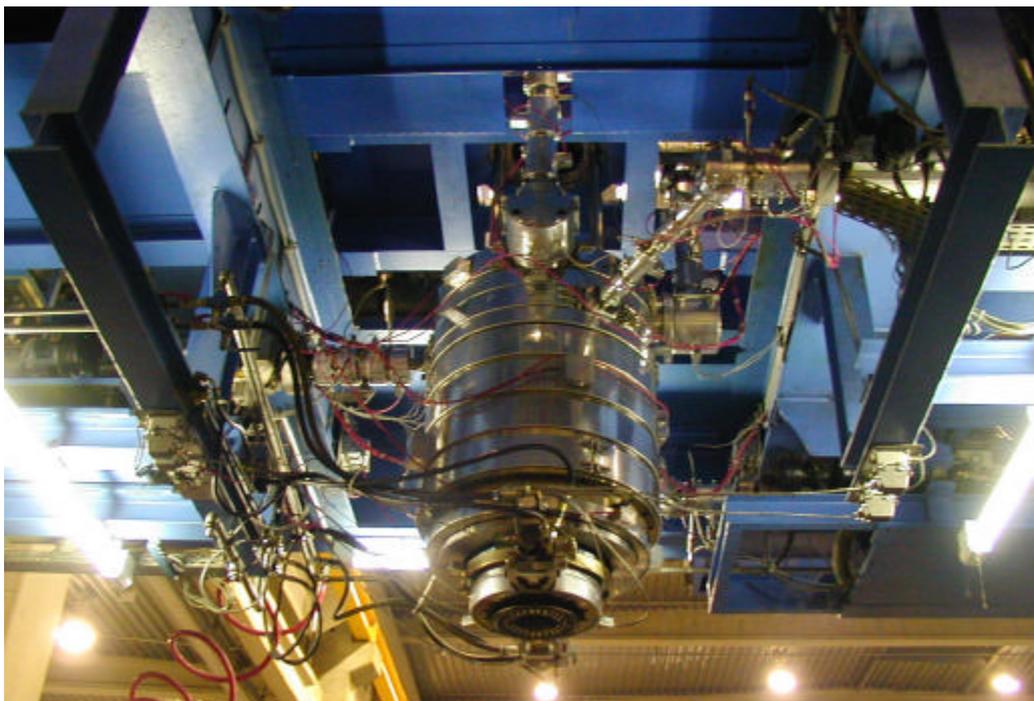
6-Schicht-Wendelverteiler-Schlauchkopf in einer umgebauten Tankblasanlage
